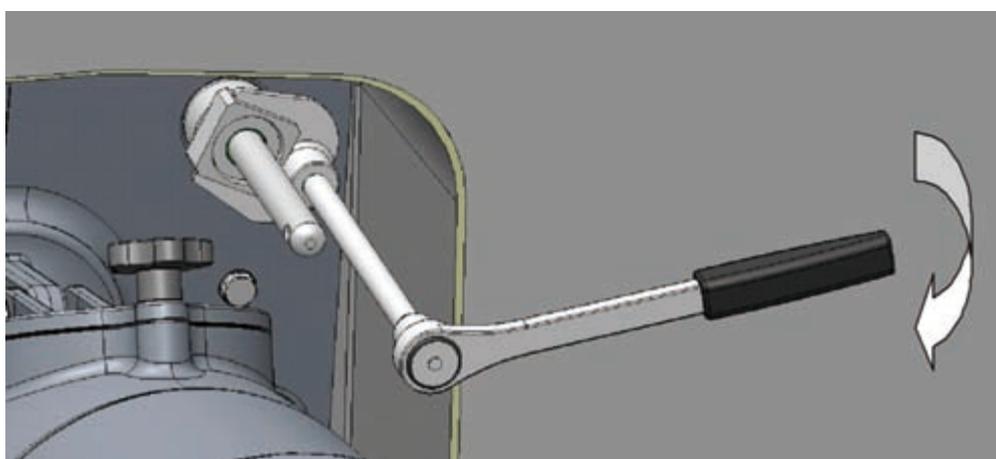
Гайка и разделитель гидравлического цилиндра
